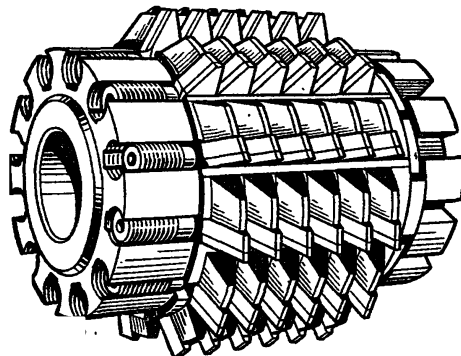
Червячная сборная острозаточенная твердосплавная фреза
